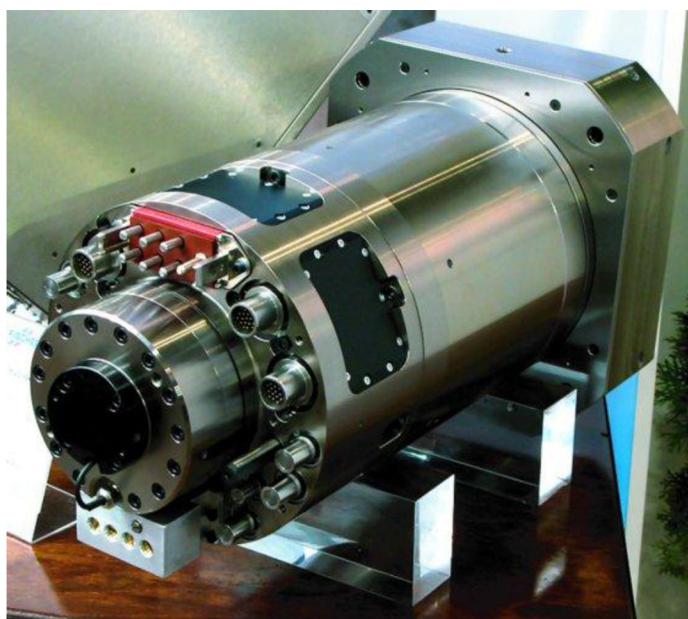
Elektrovřeteno od firmy Franz Kessler [10]
